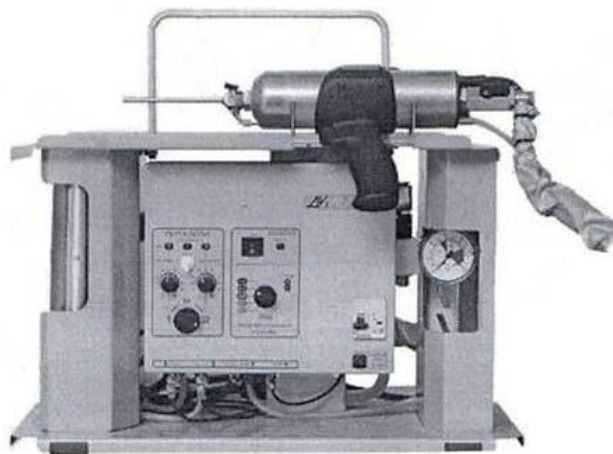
Установка ДИМЕТ Д 404 для газодинамического напыления порошков
